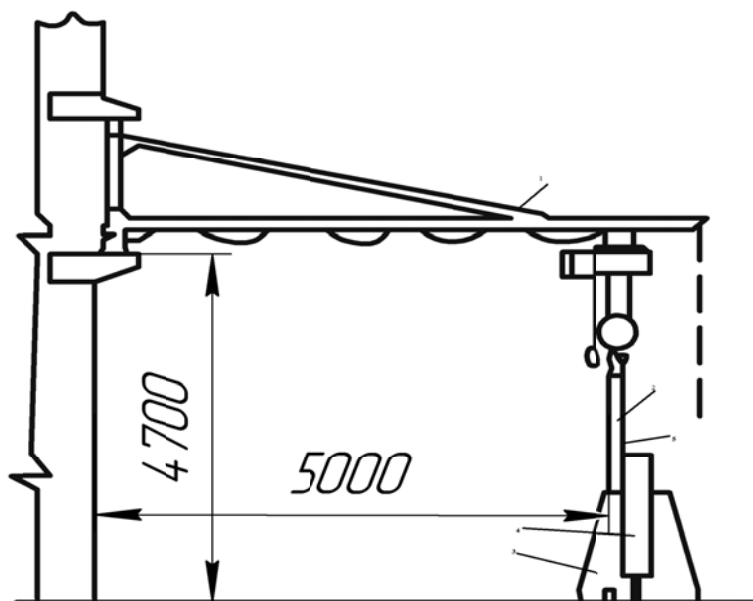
Консольно-поворотный кран для установки изделия на сварочный стенд:
